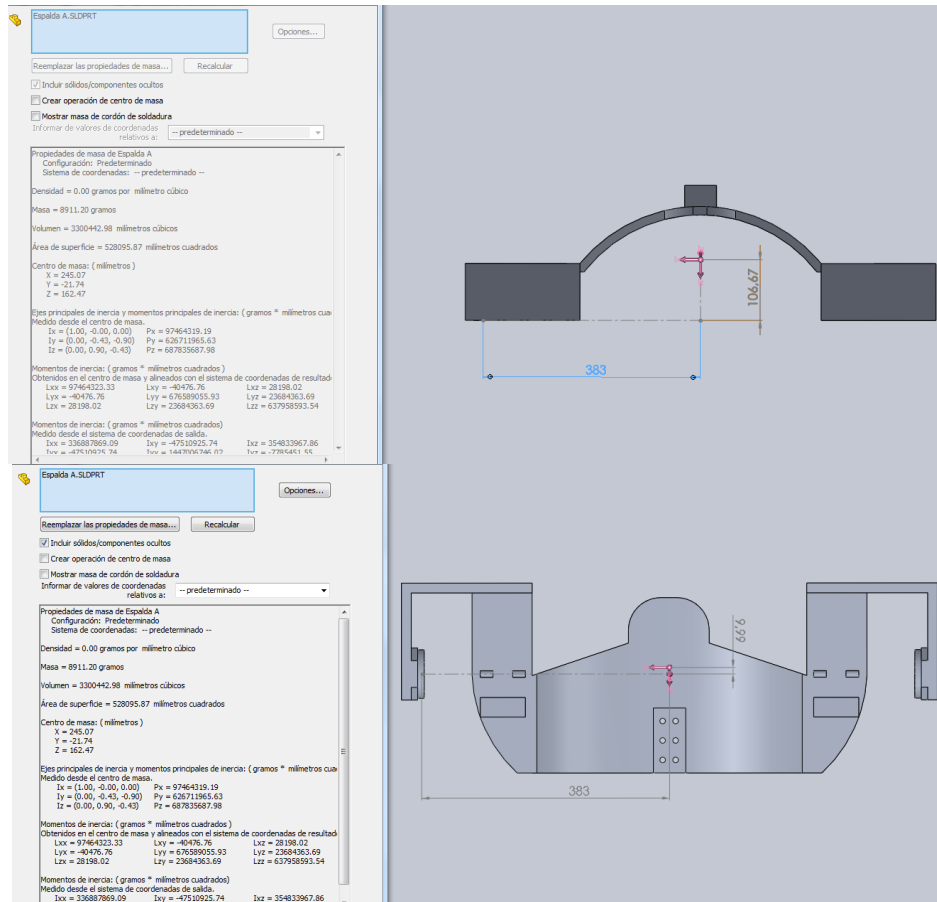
Centro de masa del ensamblaje de sección A de la espalda
